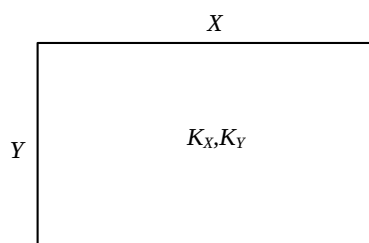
Вычисление коэффициента усадки для всей заготовки
